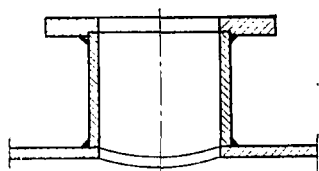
Правильная сварка патрубков с обечайкой корпуса электродуговым методом.
